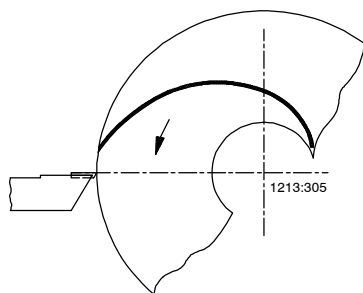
Направление вращения при обтачивании сварного колеса из хромникелевой стали
